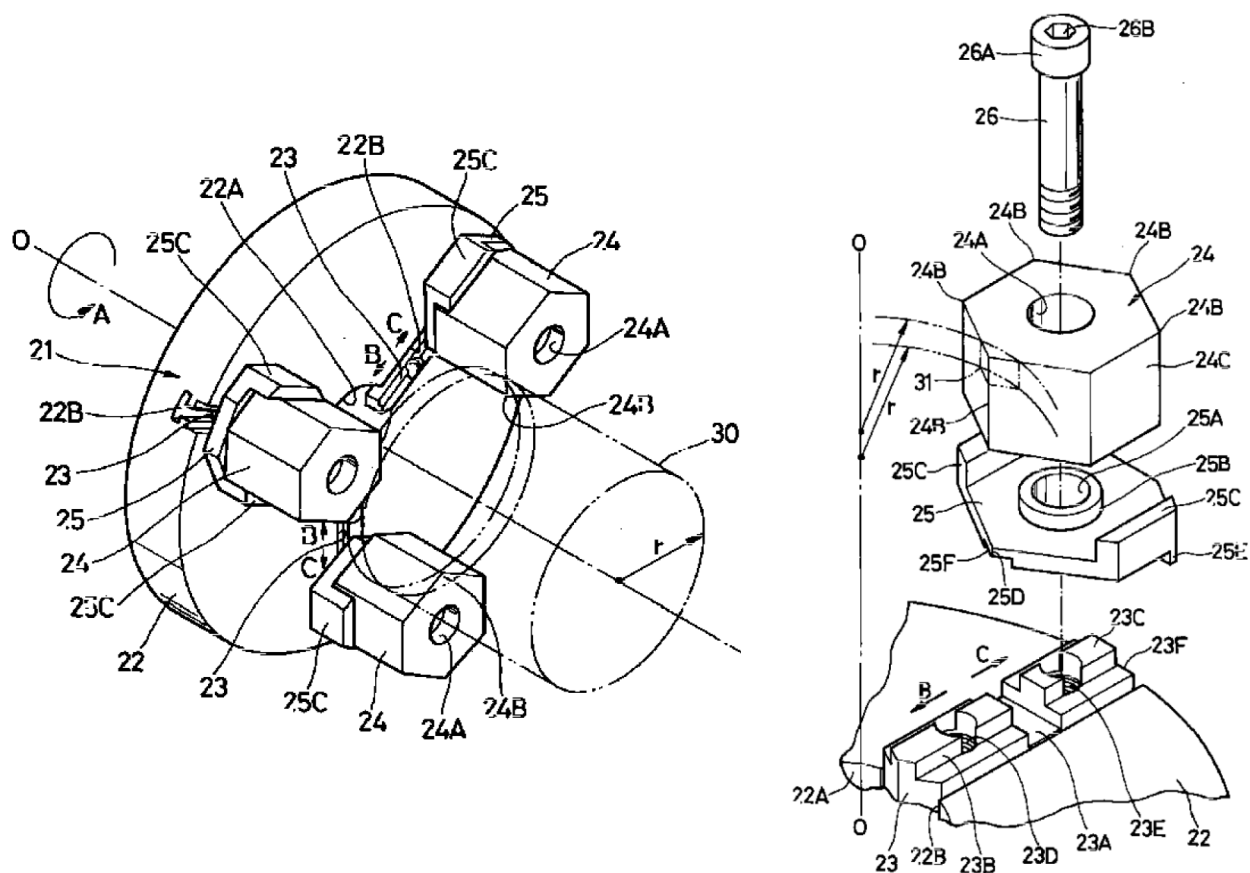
Токарний патрон із багатопрофільними затискними елементами призматичного типу
